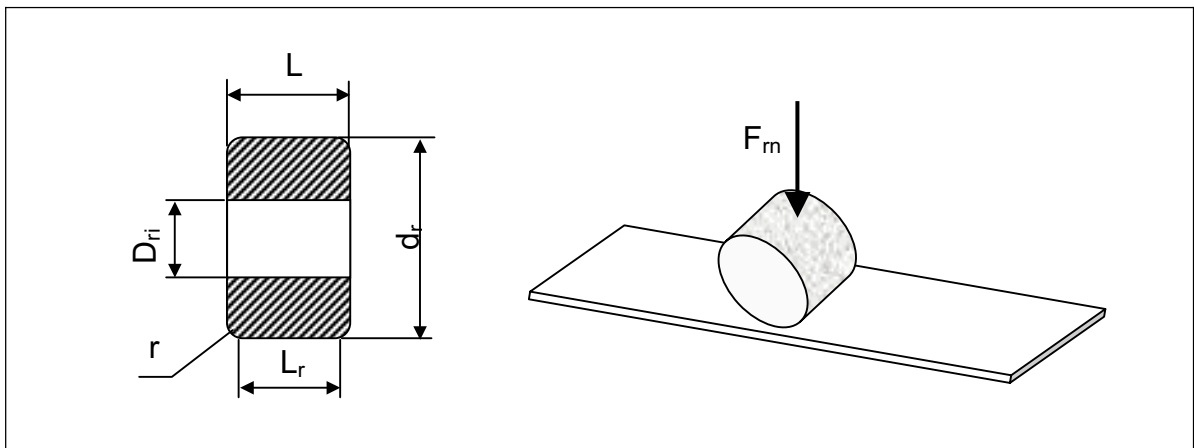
Carga de compressão externa atuante sobre a roda e dimensões principais da roda.
